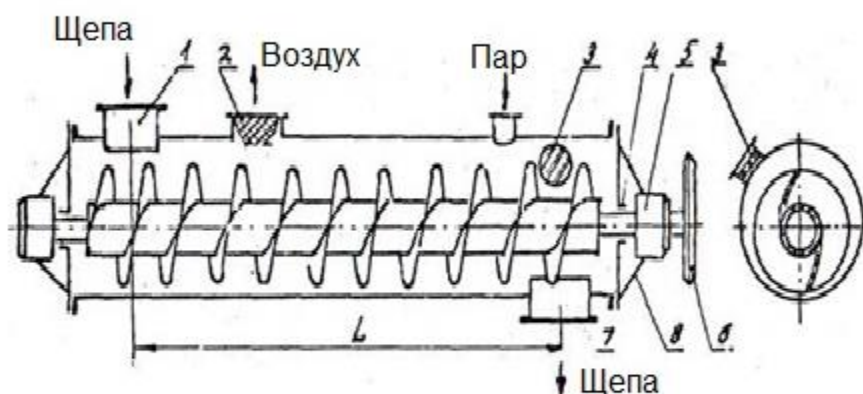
Пропарочная цистерна: 1-патрубок для подачи щепы; 2-патрубок с сеткой; 3-смотровое окно; 4-сальник; 5-подшипник; 6-звездочка привода; 7-патрубок для выхода щепы; 8-укосины для крепления подшипников
